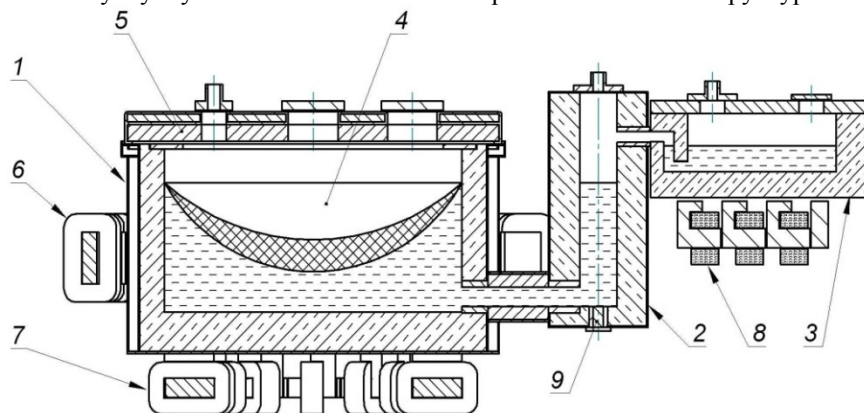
Многофункциональный плавильный агрегат: 1 – плавильный агрегат, 2 – вспомогательный резервуар, 3 – накопитель жидкого металла, 4 – плавильная камера, 5 – крышка плавильной камеры, 6, 7, 8 – МГД-генераторы, 9 – выпускное отверстие.
